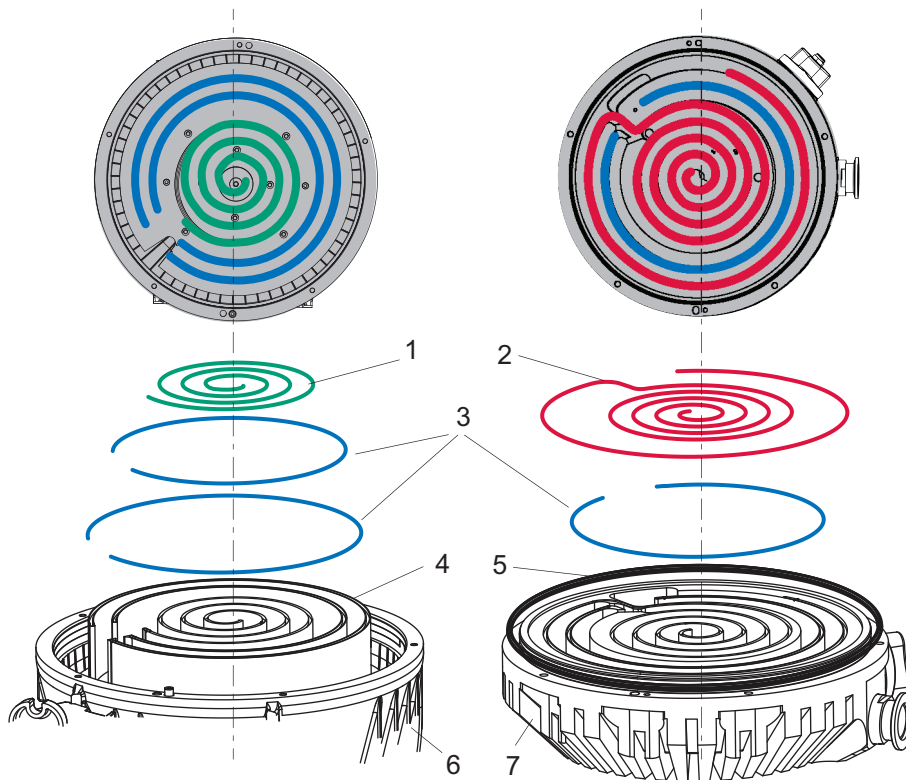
Remplacement des joints d'extrémité sur la pompe scroll
